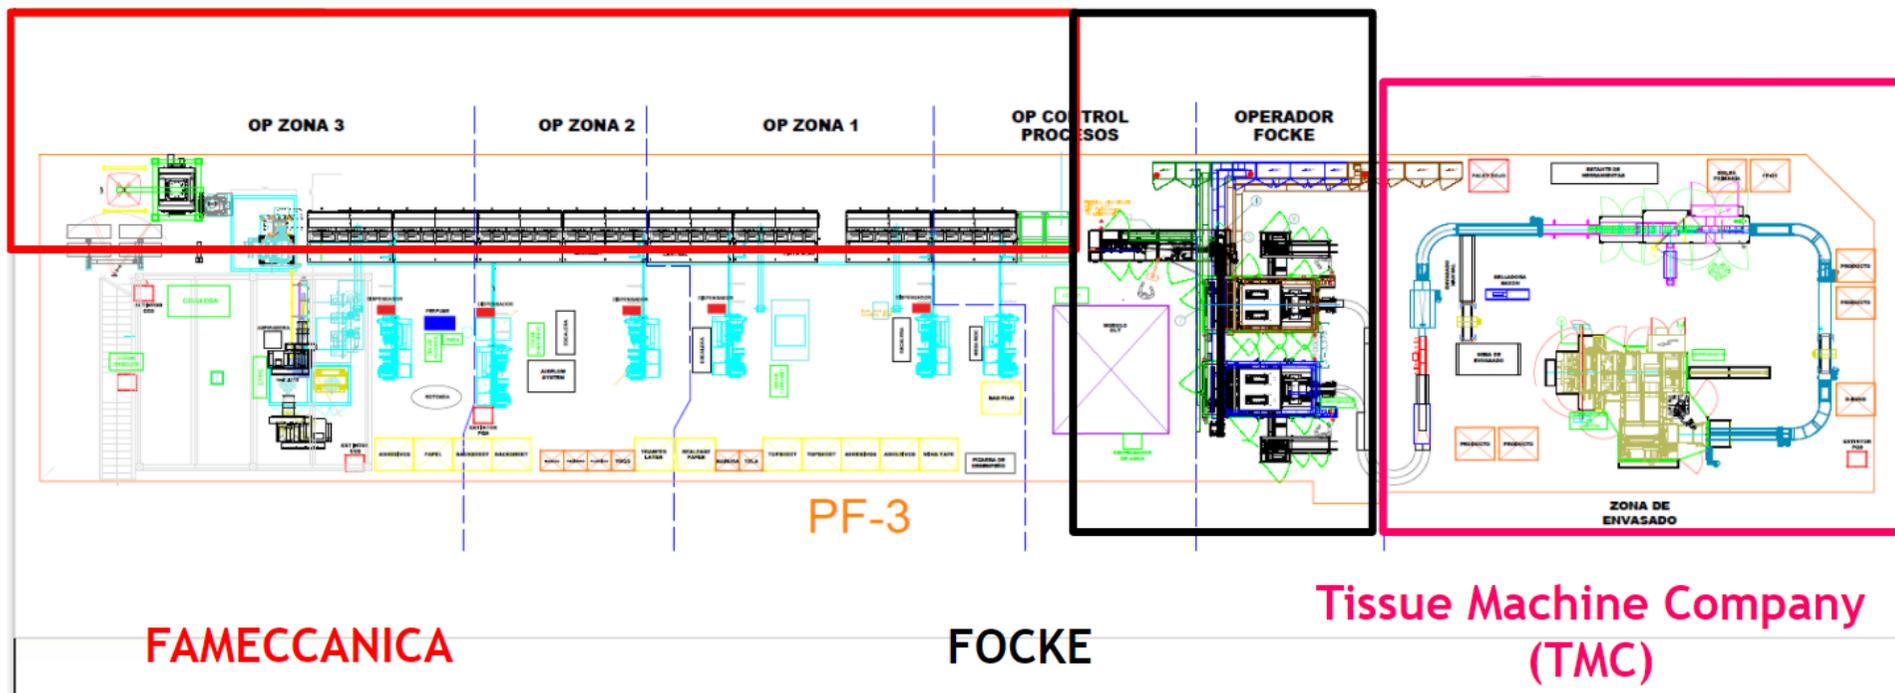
Plano de máquina de toallas higiénicas (PF3)
